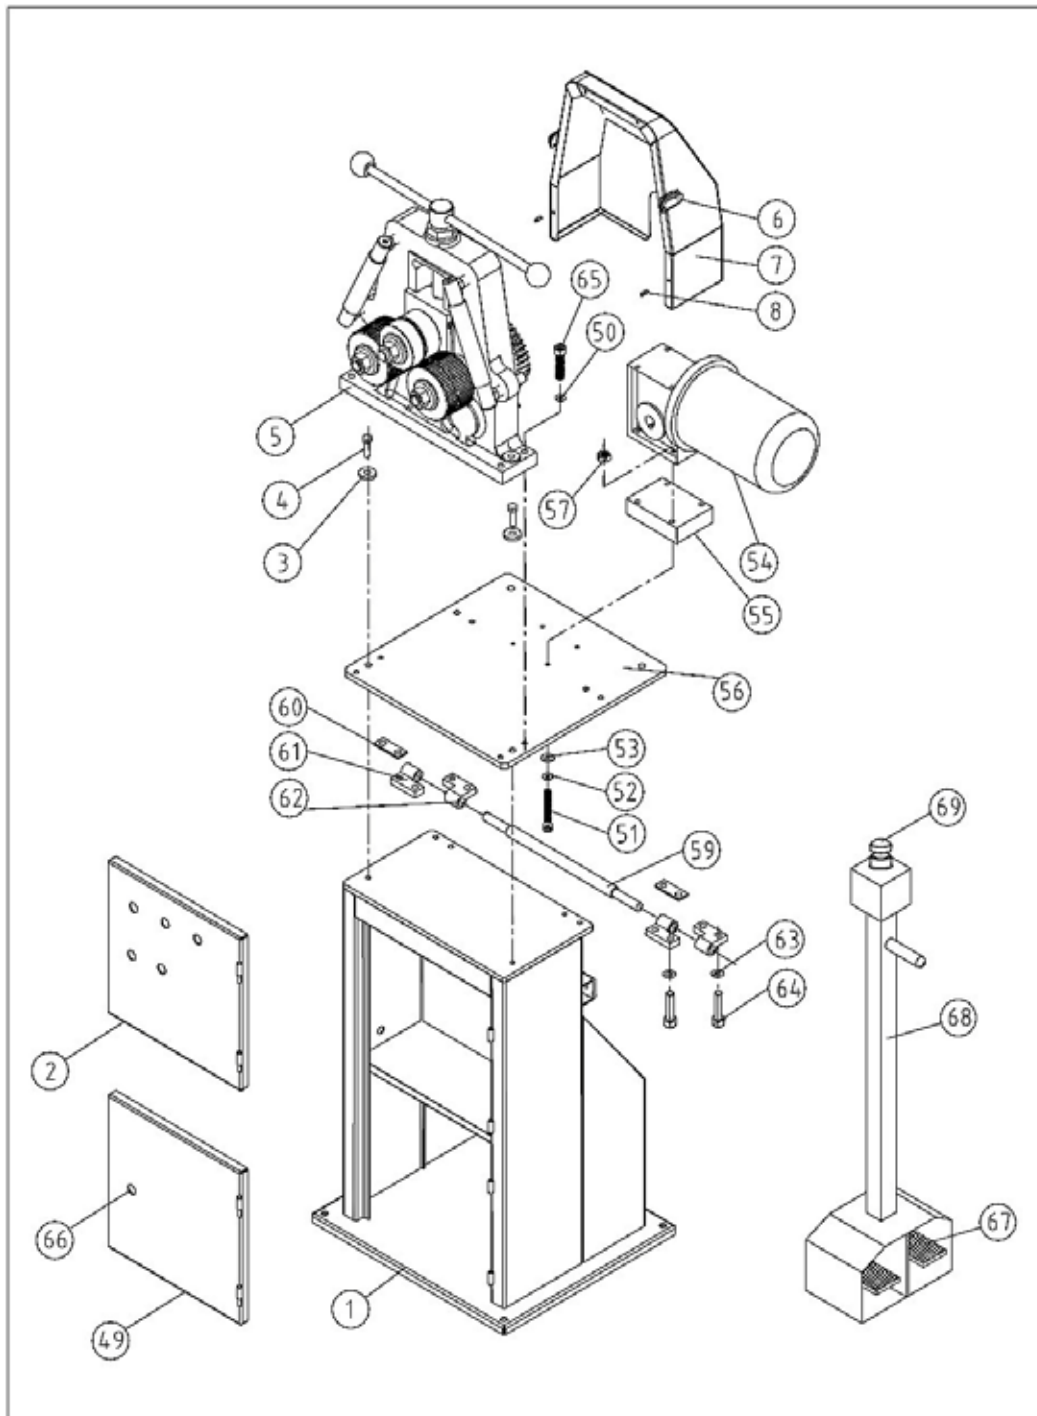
Vue éclatée 1 - Châssis et cadre PRM 10 E
